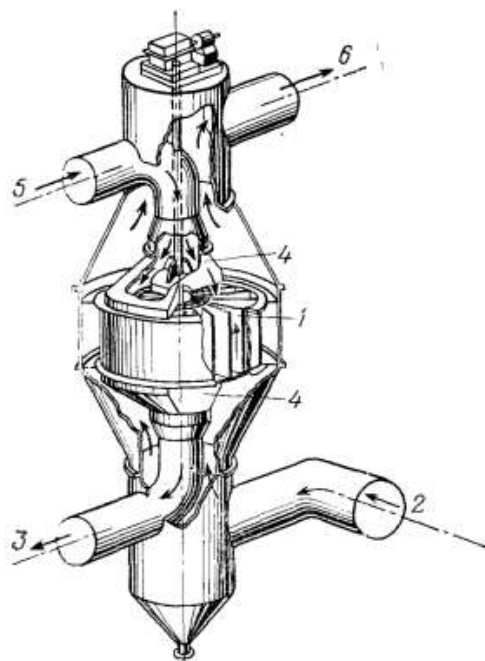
Регенеративный воздухоподогреватель типа Ротемюле: 1 – неподвижная насадка; 2 – вход дымовых газов; 3 – выход воздуха; 4 – вращающийся воздушный патрубок; 5 – вход воздуха; 6 – выход дымовых газов
